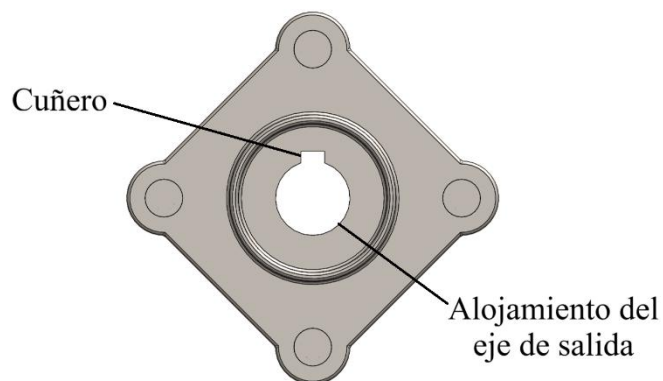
Modelo geométrico CAD 3D del cubo de la rueda en una vista frontal.
